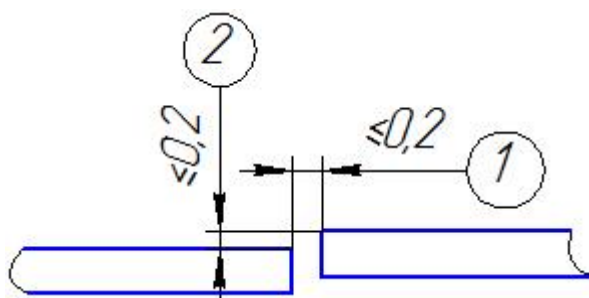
Параметры, контролируемые при сборке образцов под сварку
